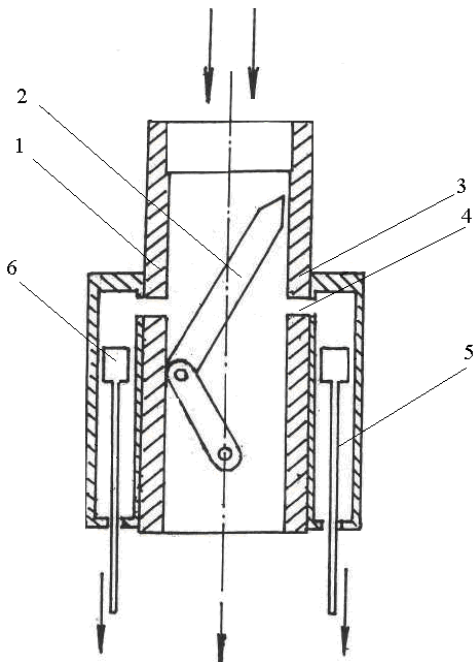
Пристрій для руйнування і видалення піщаного корка
